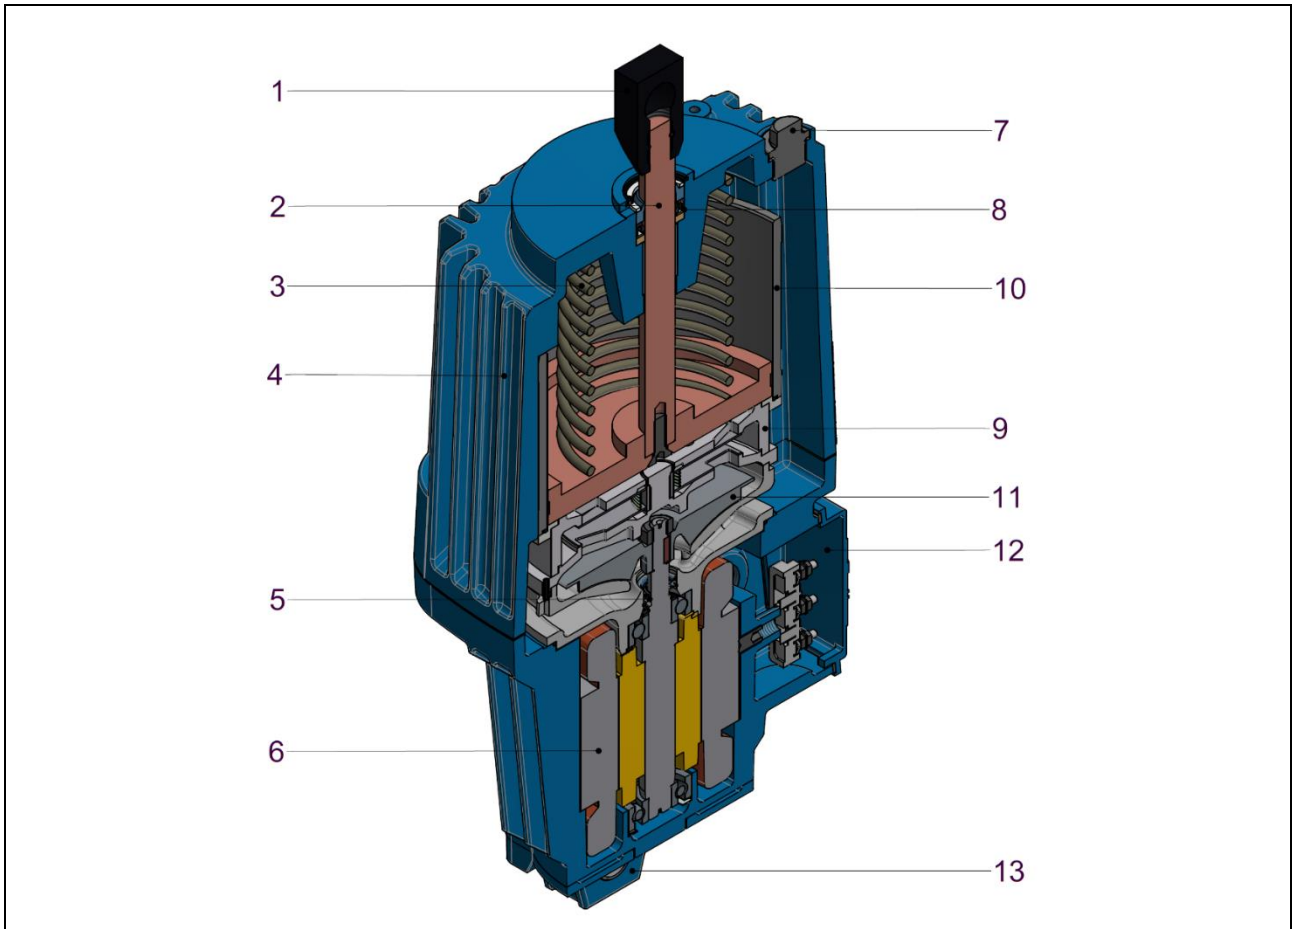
Конструкция устройства ELDRO® ED500 / ED1250
